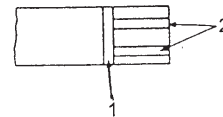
Плунжер с дополнительной кольцевой канавкой: 1 - кольцевая канавка; 2 - прорези для впуска топлива.
